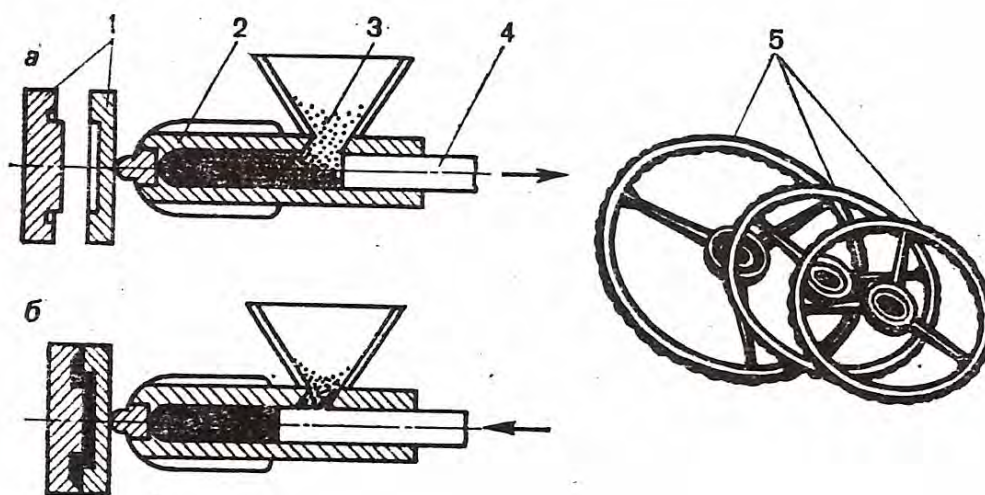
Схема работы литьевой машины: а - разогрев полимер; б - формование; 1 – пресс-форма; 2 - нагревательный цилиндр; 3 – полимер; 4 – поршень; 5 - рулевые колеса.
